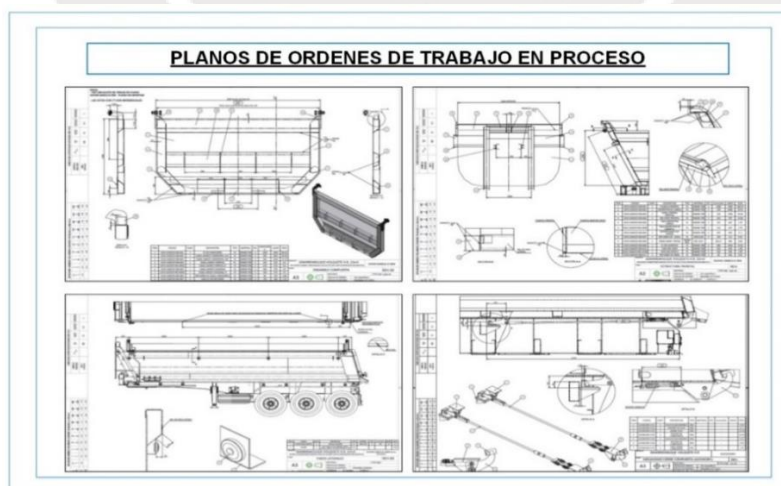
Pizarra de corcho con planos de órdenes de trabajo en proceso
